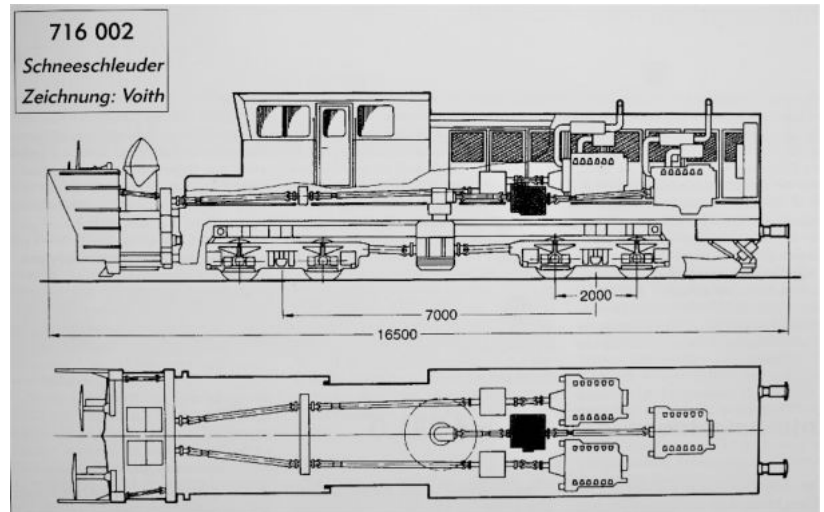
Zeichnung der Motoren/Antriebe in 716.002 Aus: Arend Boldt, Bahndienstfahrzeuge
